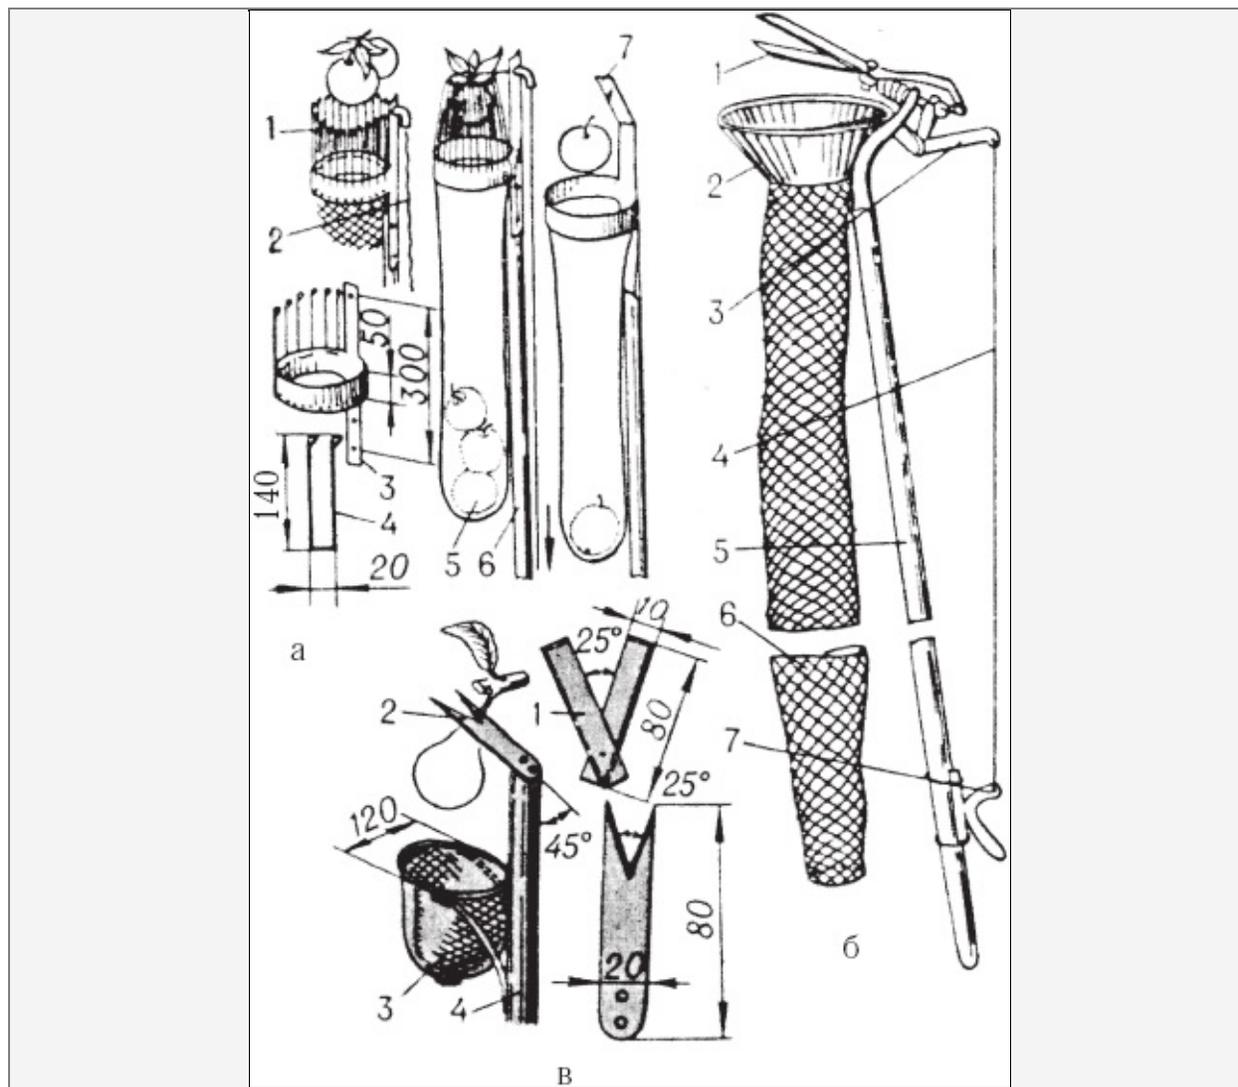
Устройство для сбора плодов: а – сниматель фруктов: 1 – клетка с подвижными стенками; 2 – шнур; 3 – кольцо клетки; 4 – прутья; 5 – мешочек; 6 – шест; 7 – нож; б – плодосъемник с ножницами: 1 – ножницы; 2 – приемная часть; 3 и 7 – рычаги; 4 – трос; 5 – шест; 6 – длинный рукав; в – плодосъемник: 1 – планка с лезвием; 2 – нож захват; 3 – мешочек для плода; 4 – шест
